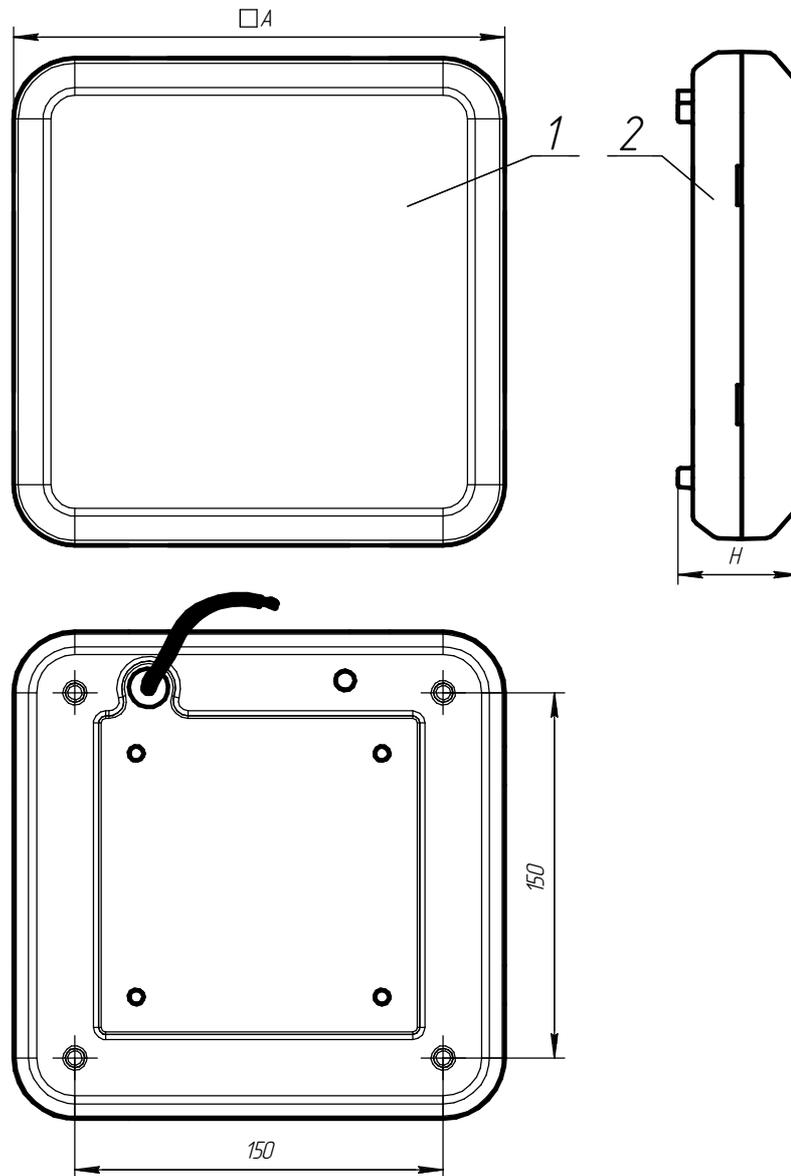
Общий вид, габаритные и присоединительные размеры светильника ДБО91.
